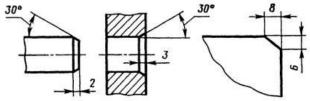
Нанесение размеров фасок линейными угловыми размерами или двумя линейными размерами
